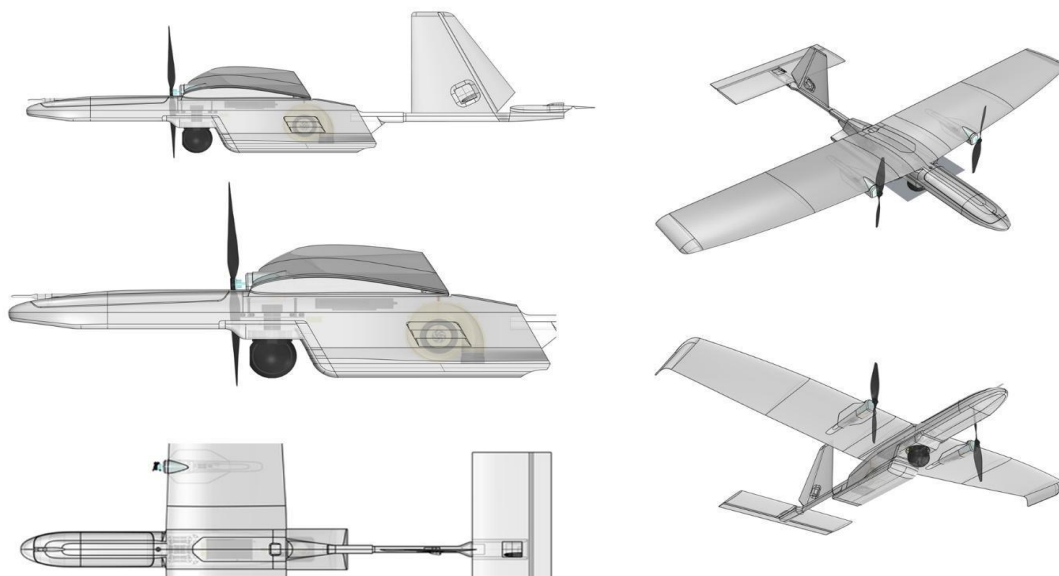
Внешний вид беспилотного летательного аппарата
